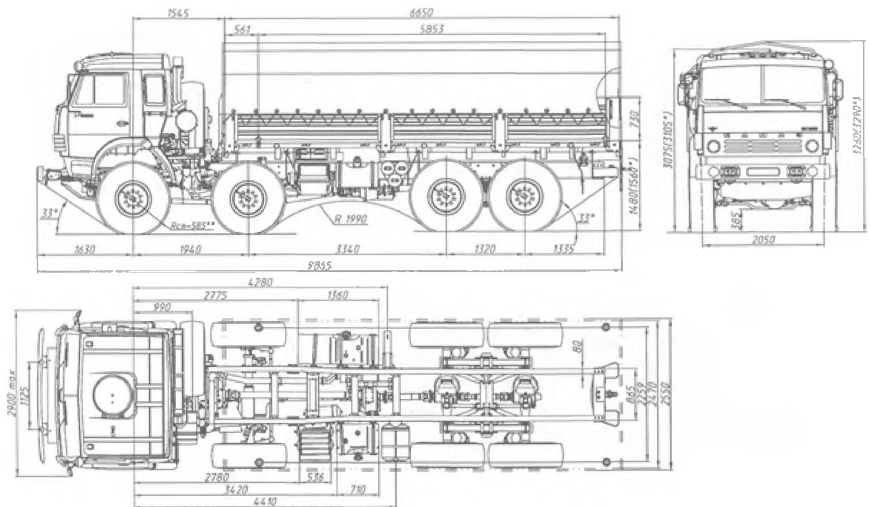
Автомобиль-тягач КАМАЗ-63501. Габаритные размеры
